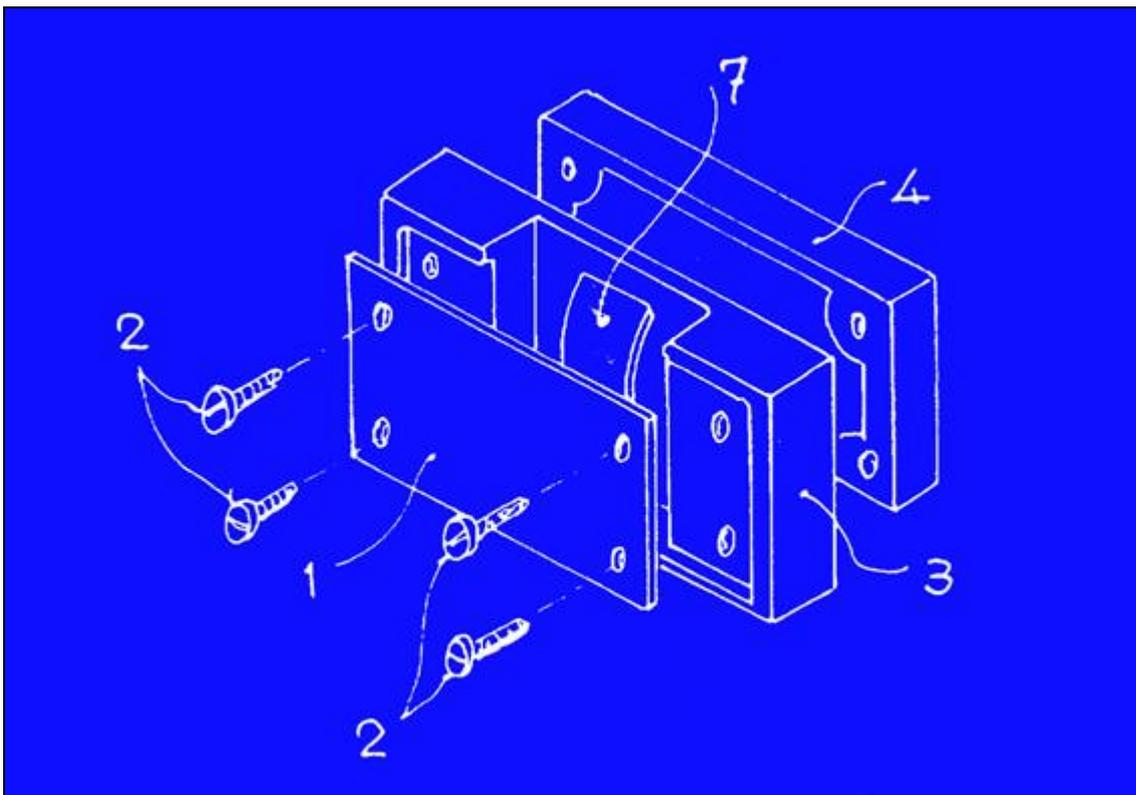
Plano del soporte (Arch. J.M. Sanchis)
